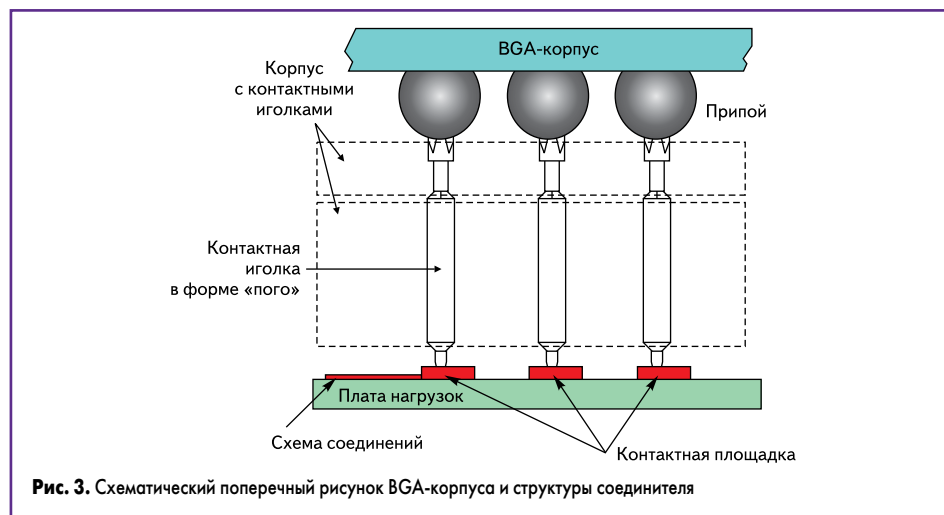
Схематический поперечный рисунок BGA-корпуса и структуры соединителя
